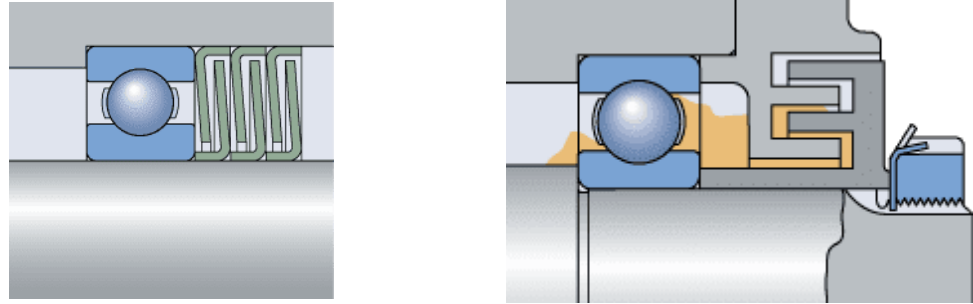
Конструкції лабіринтів-ущільнювачів для підшипників кочення
